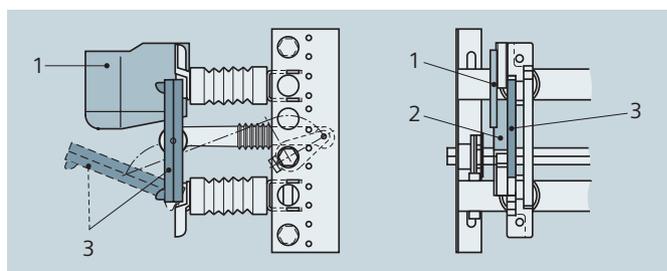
выключатель-разъединитель ЗСД2: (1) плоская автогазовая дугогасящая камера, (2) контактный нож, (3) вспомогательный нож
